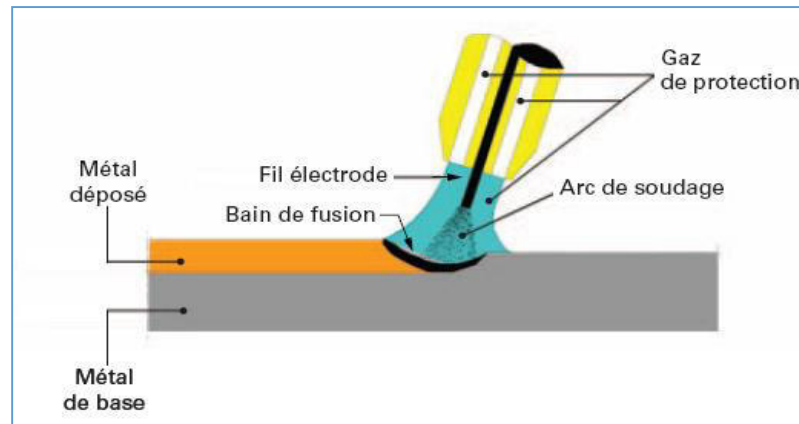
Principe de soudage sous flux gazeux [17].
